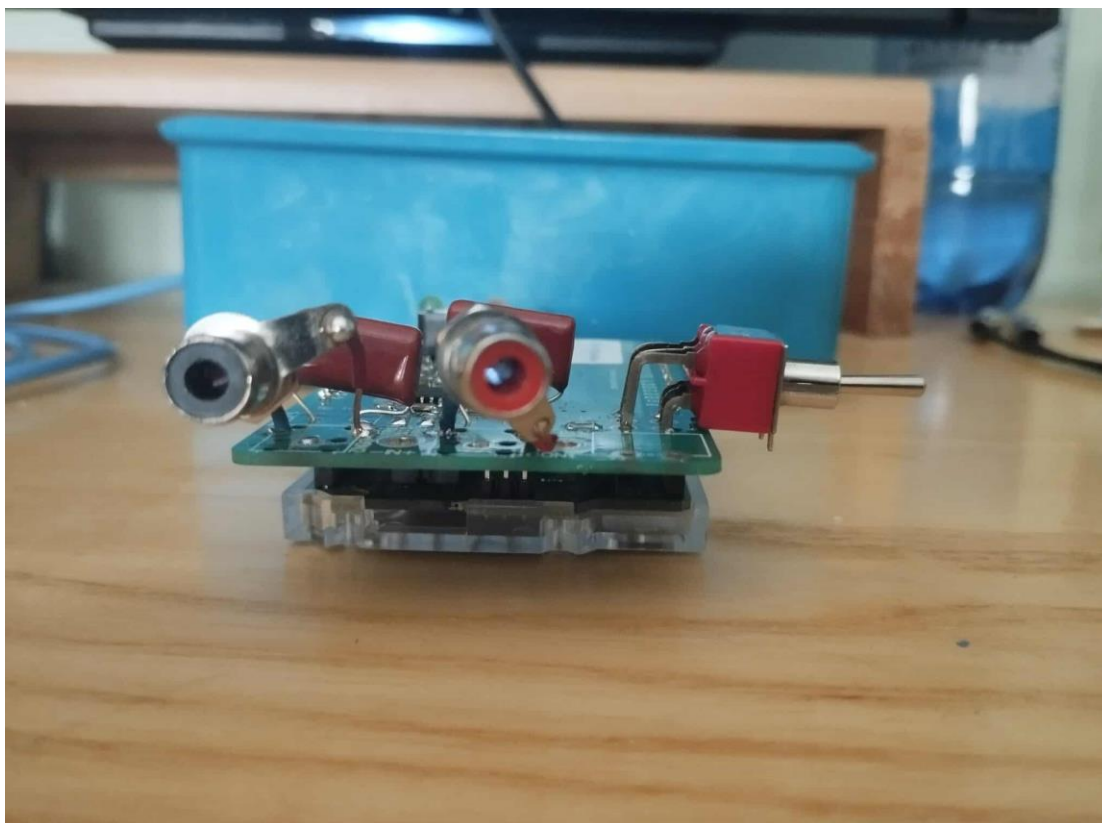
Κάτοψη της pcb πλακέτας
